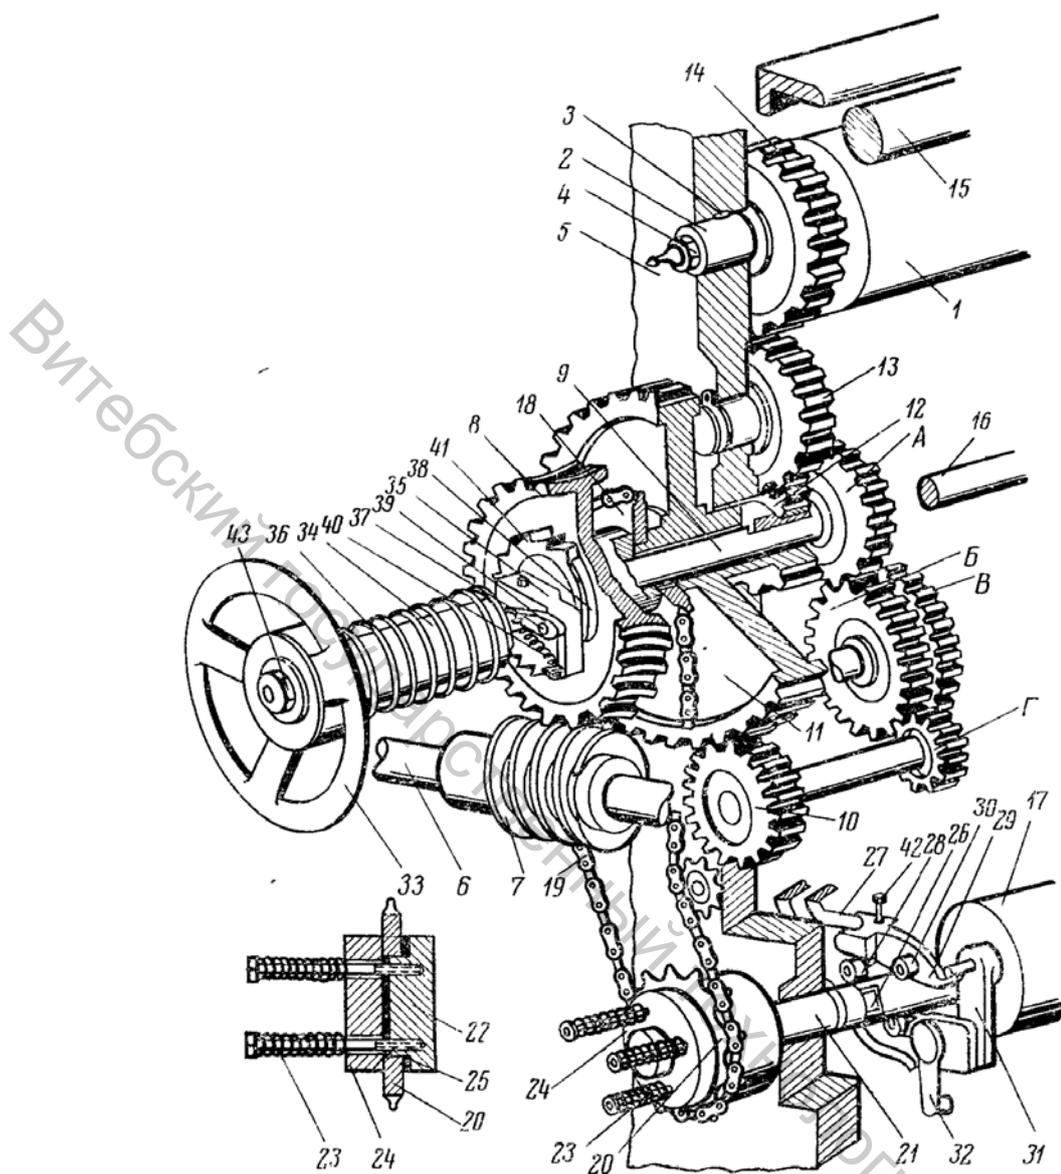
Товарный механизм ткацкого станка СТБ
